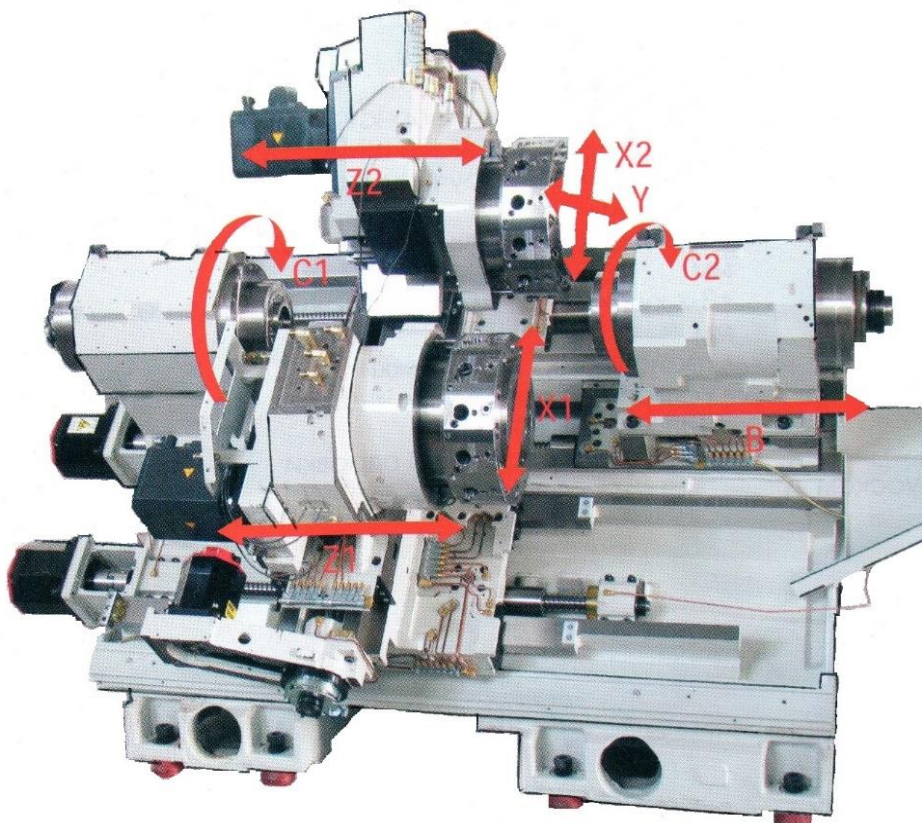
Двошпиндельний токарний верстат з ЧПК фірми Microcut Challenger
